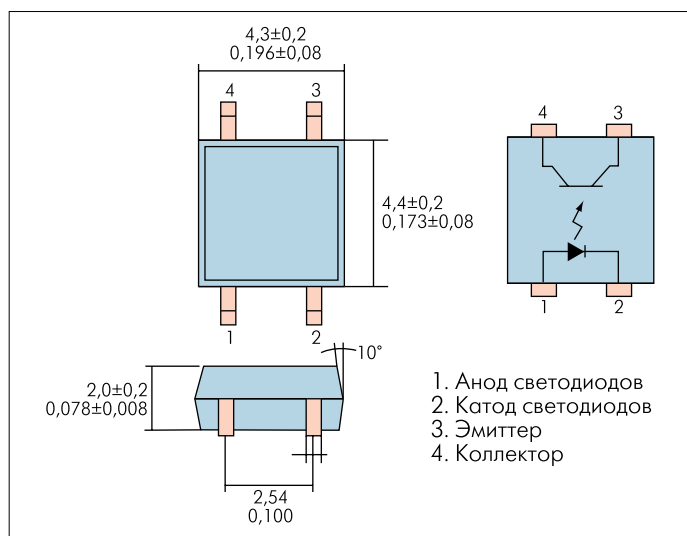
Размеры корпуса и назначение вывода транзисторной оптопары PB181S
